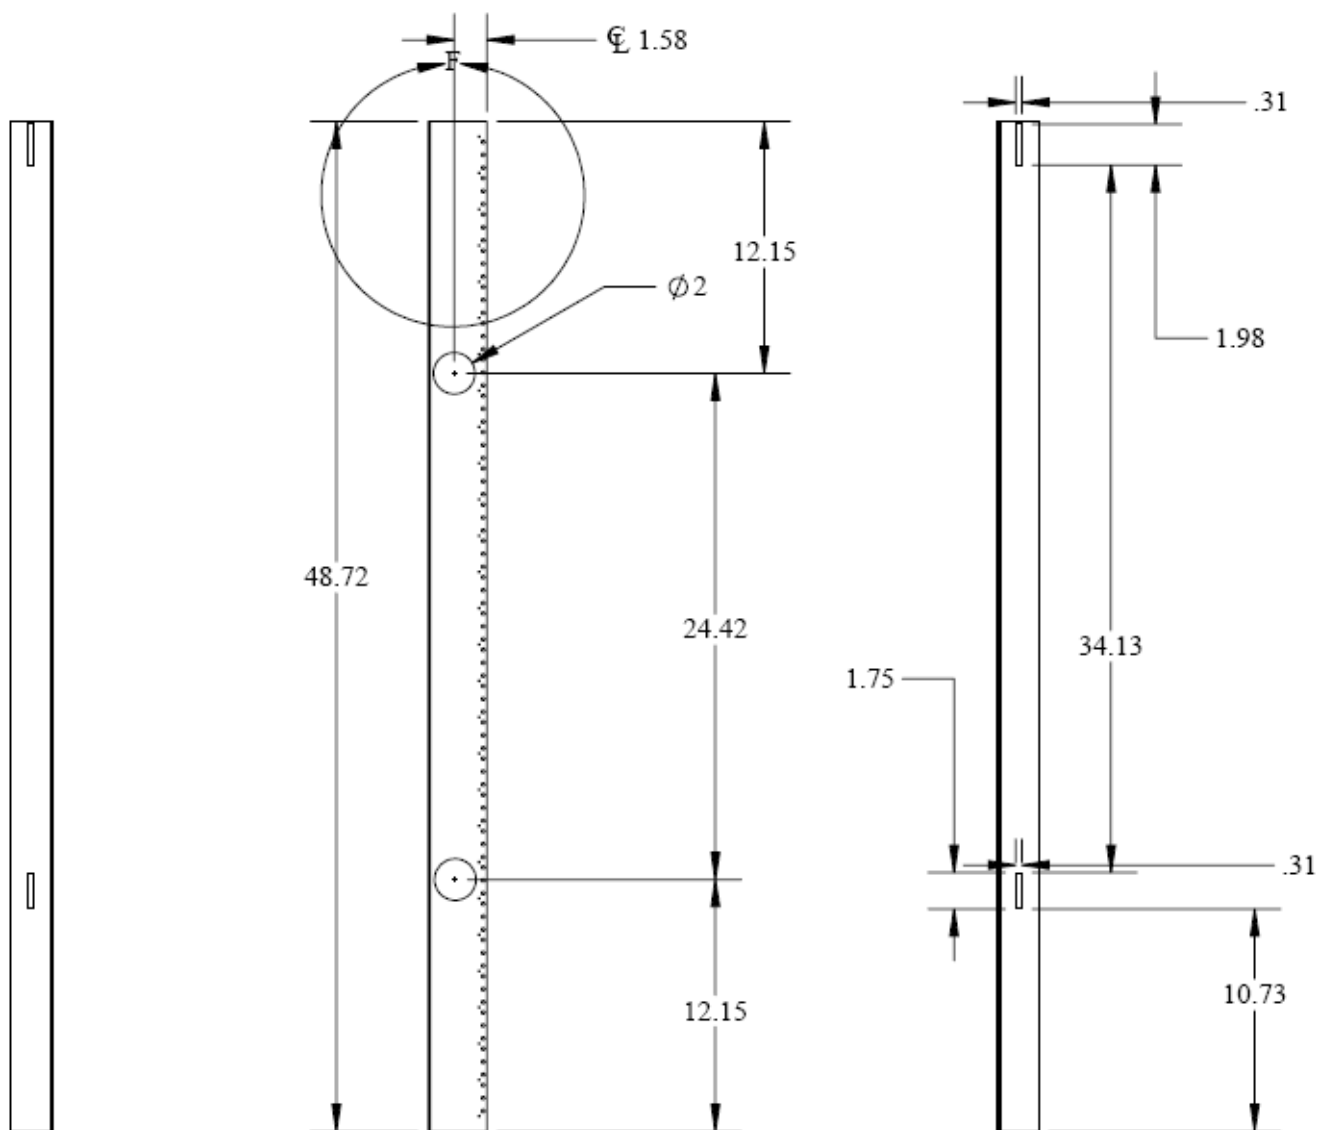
DETALLES DE RIEL DE RACK: TENGA EN CUENTA QUE EL DETALLE "F" ESTÁ EN LA PÁGINA SIGUIENTE.
